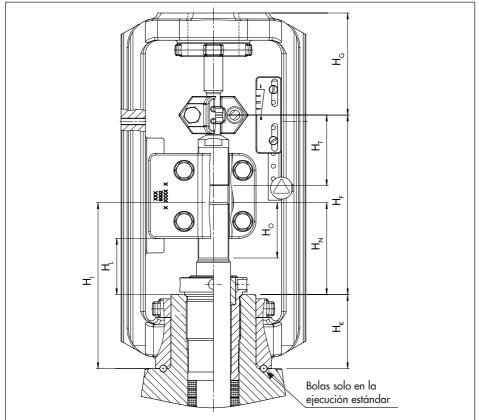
Dibujo dimensional con dimensiones de montaje de los accionamientos neumáticos Tipo 3271 y Tipo 3277
